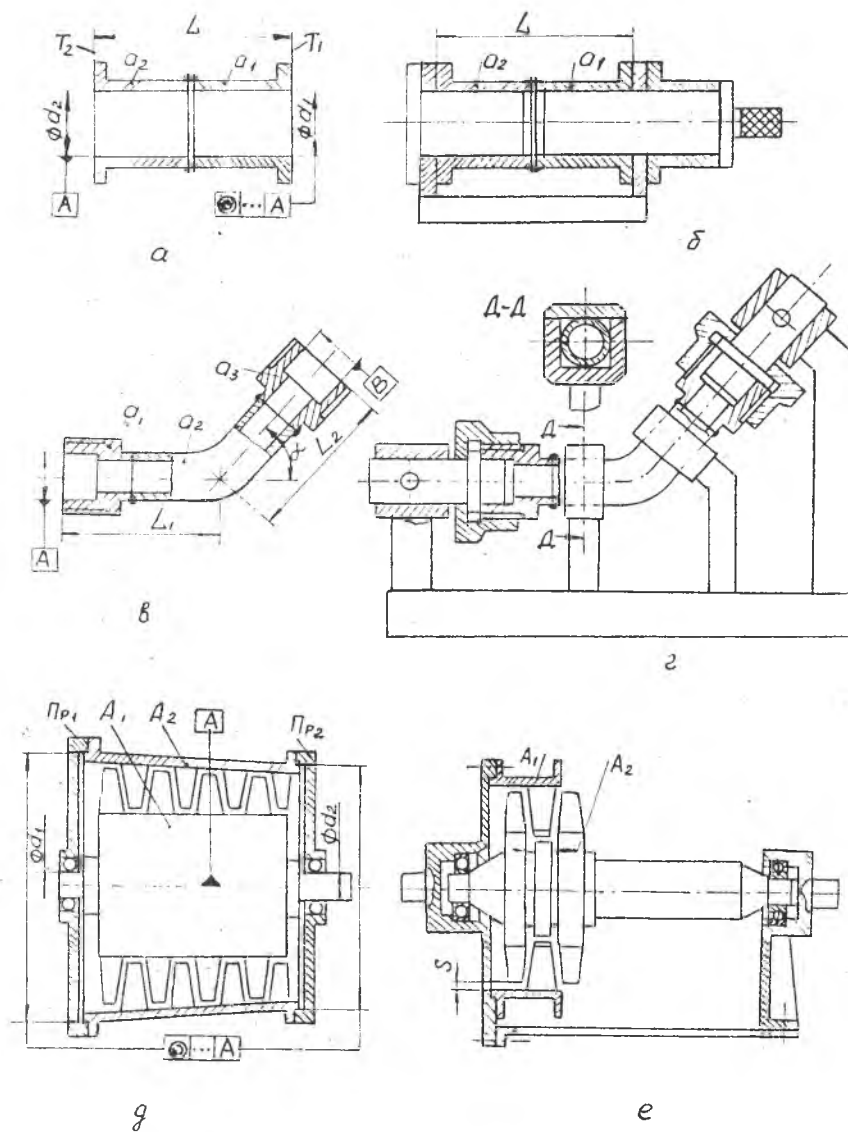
Примеры базирования элементов изделия с помощью поверхностей сборочного приспособления
